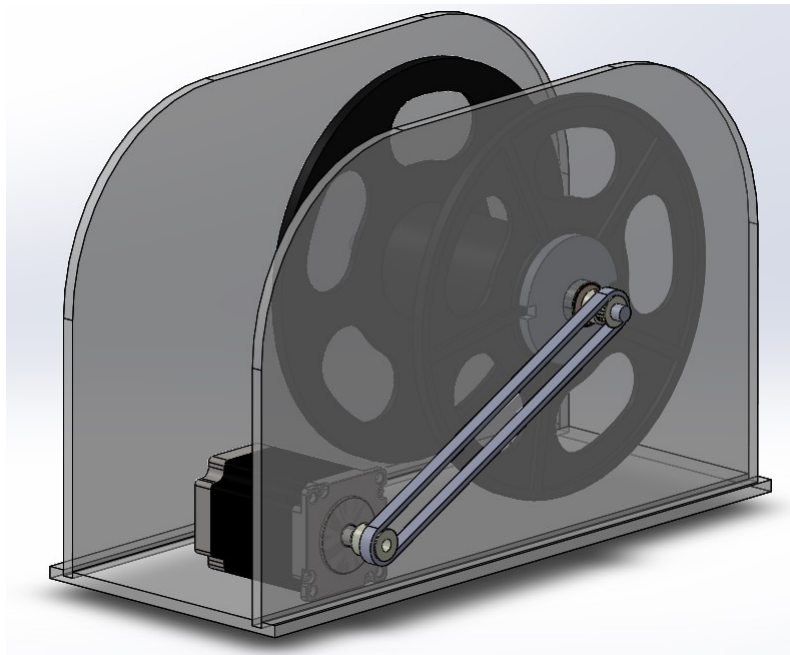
Diseño conceptual en CAD del cabrestante automático.
